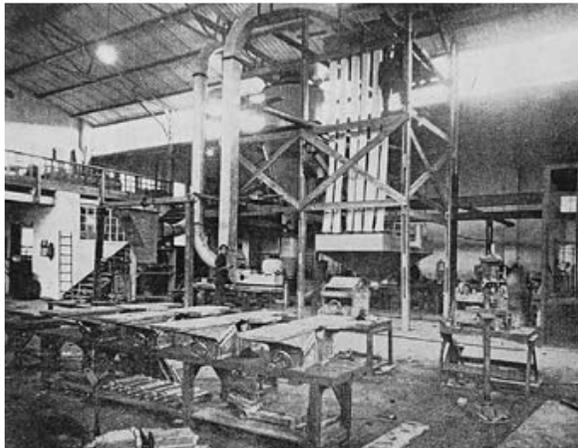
fábrica de construcción de elementos prefabricados de la época
